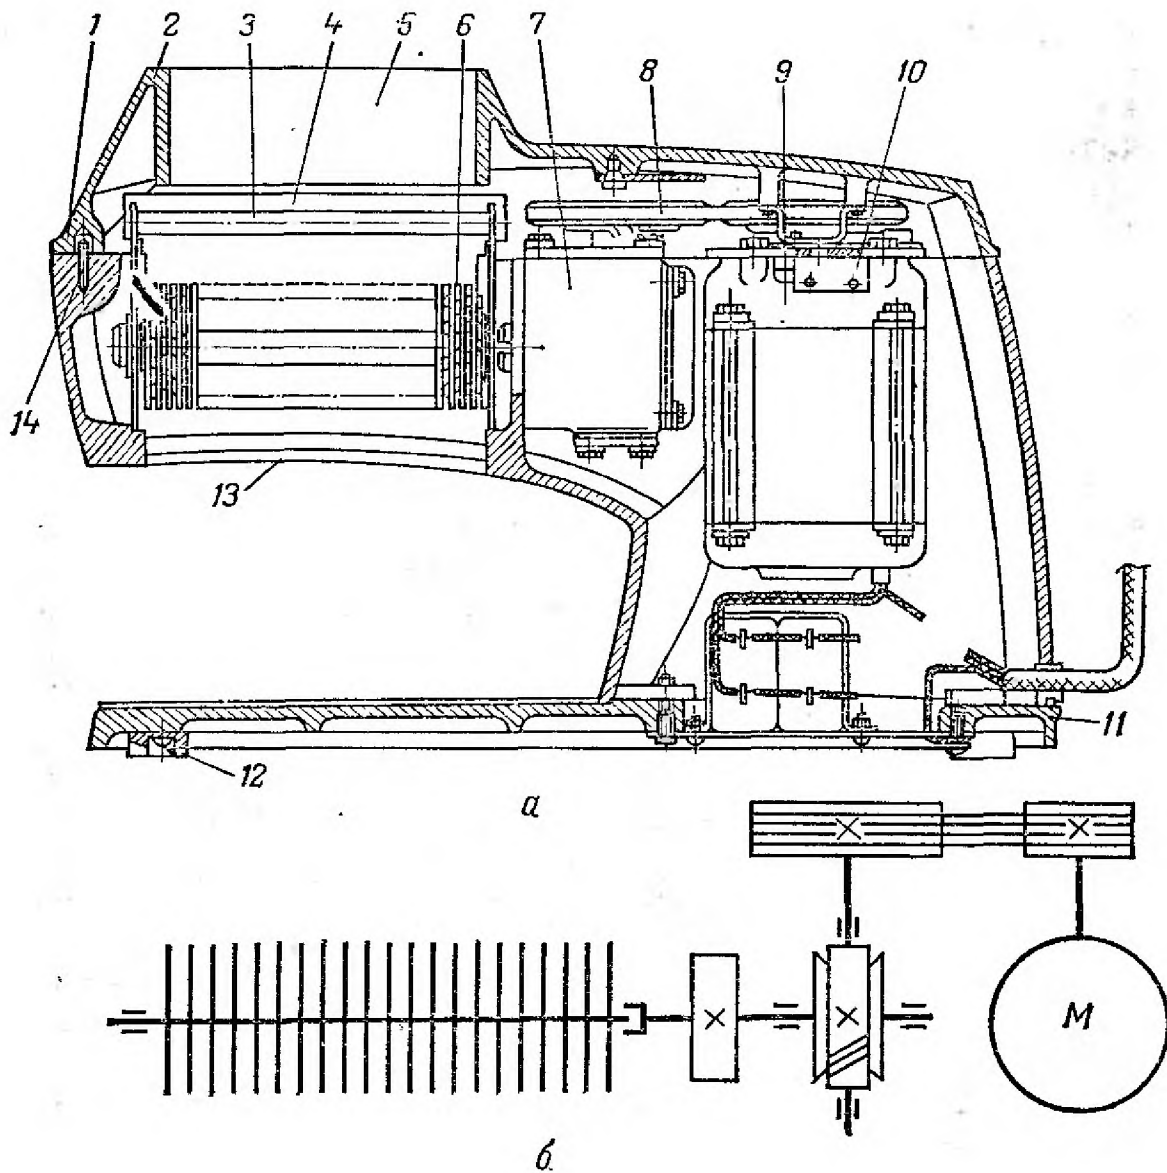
М'ясорозпушувач МРМ-15: а – загальний вигляд; б – кінематична схема; 1 – корпус; 2 – кришка; 3 – каретка; 4 – гребінки очищувальні; 5 – вікно завантажувальне; 6 – блоки ножові; 7 – редуктори; 8 – передача клинопасова; 9 – електродвигун; 10 – мікроперемикач; 11 – основа
